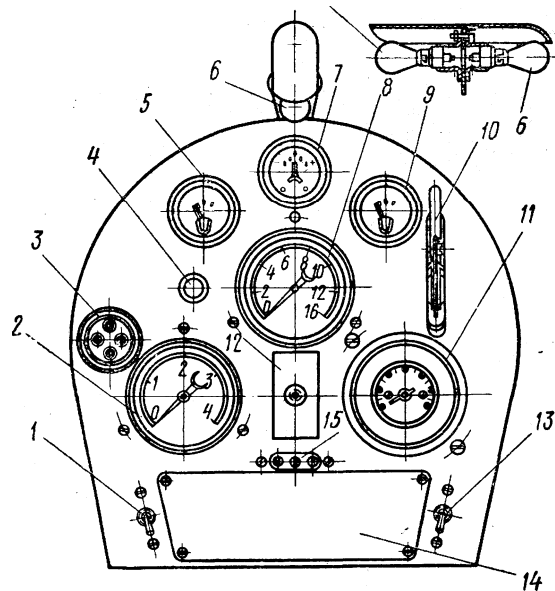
Щит керування компресорної станції ЗИФ–55:
